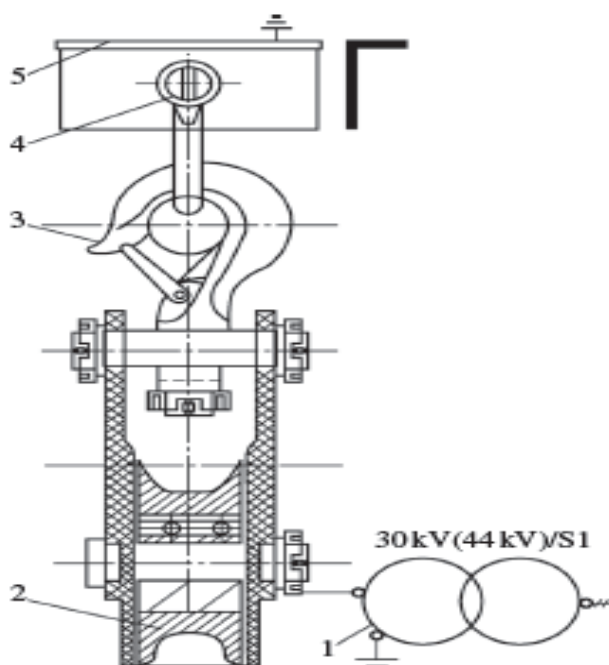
Схема устройства электрического испытания для инструмента. 1 - прибор для проверки частоты питания; 2 - шкив; 3 - подъемный крюк; 4 - I-образное кольцо; 5 - металлическая поперечина.
